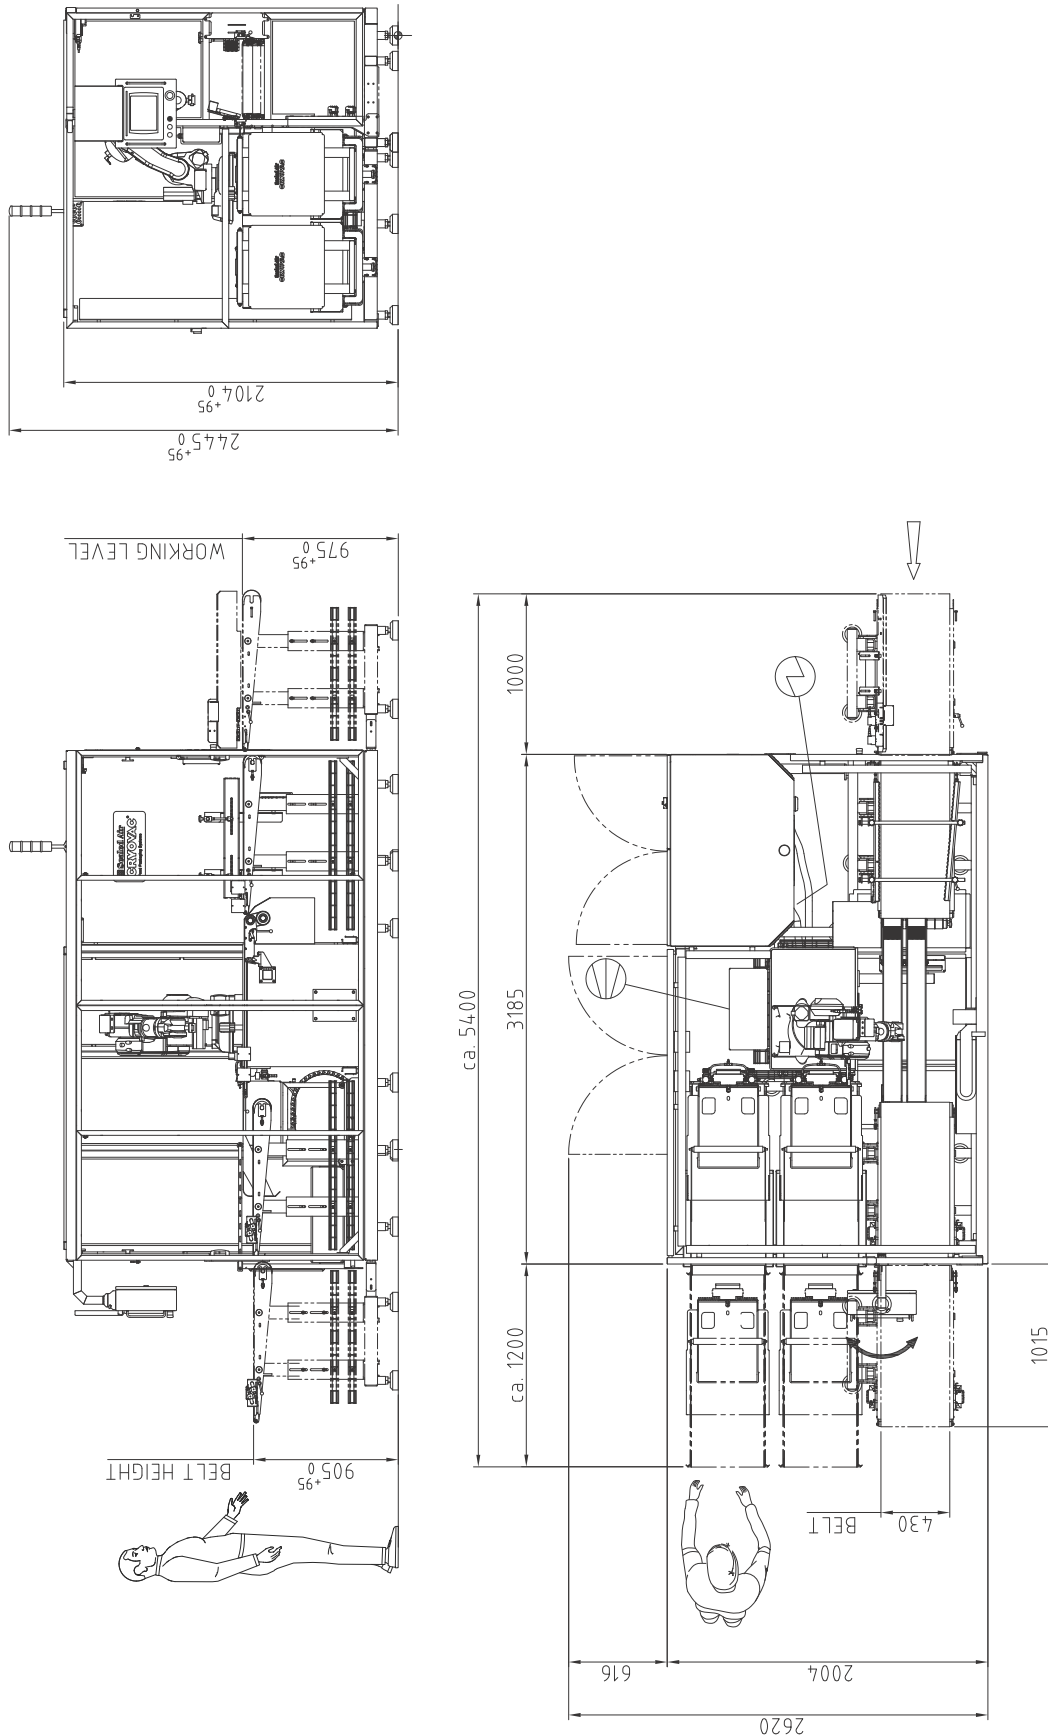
, Dimensiones RL (flujo del producto de derecha a izquierda)
